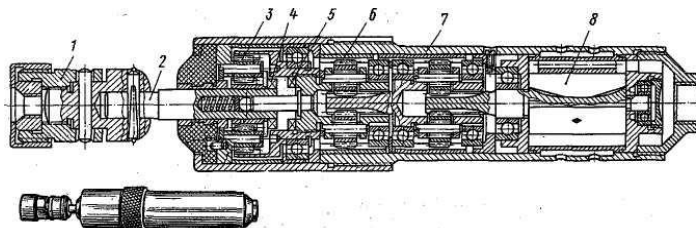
Шпильковерт ИП7201. Общий вид
